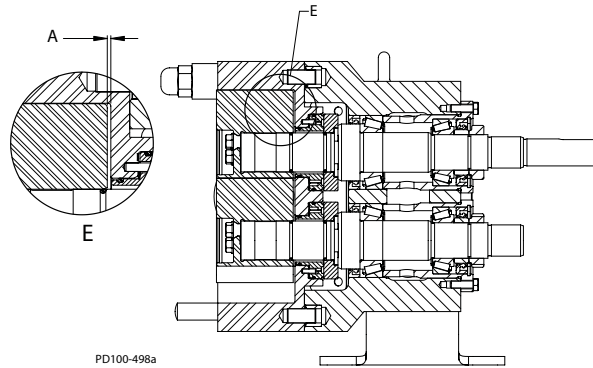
Holgura entre el rotor y el cuerpo de la bomba
